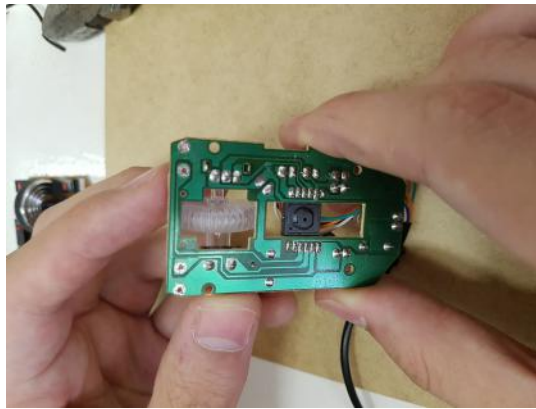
Parte posterior da PCB do mouse com os botões já removidos
